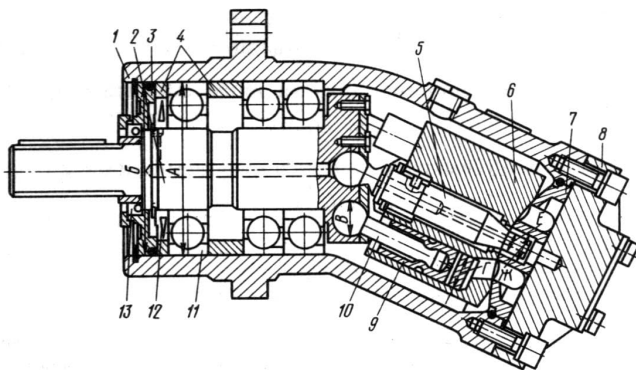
Насос-гидромотор серии 210: 1 – корпус; 2 – вал приводной; 3 – крышка передняя; 4 – втулки распорные; 5 – шип центральный; 6 – блок цилиндров; 7 – кольцо распределительное; 8 – крышка задняя; 9 – поршень; 10 – шток; 11 – подшипник; 12 – пружина тарельчатая
